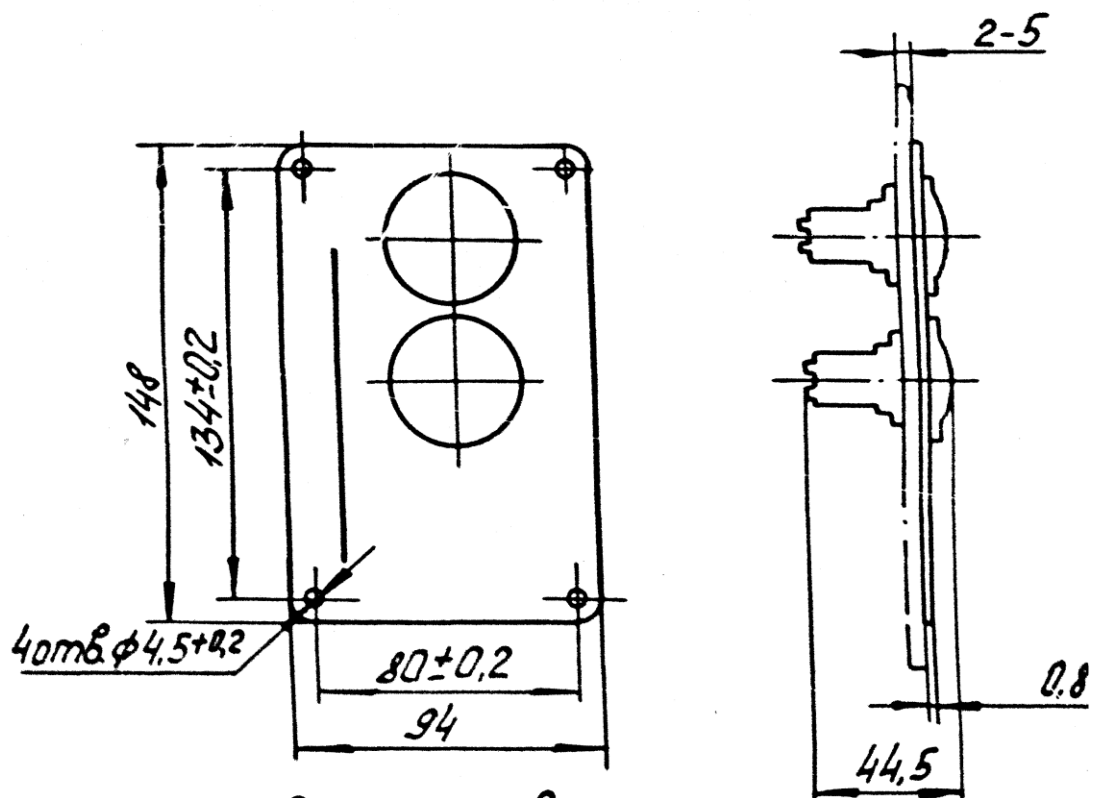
Габаритный чертеж прибора М1611 с промежуточным фланцем
